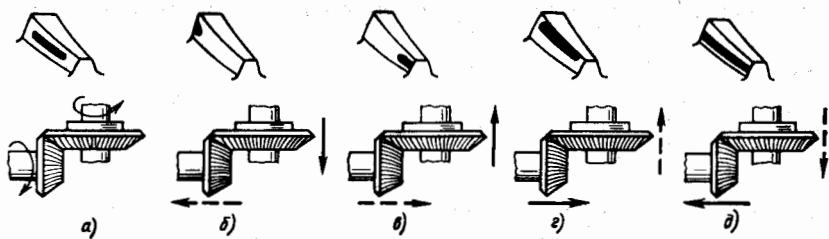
Расположение пятна контакта на зубьях зубчатого колеса главной передачи
